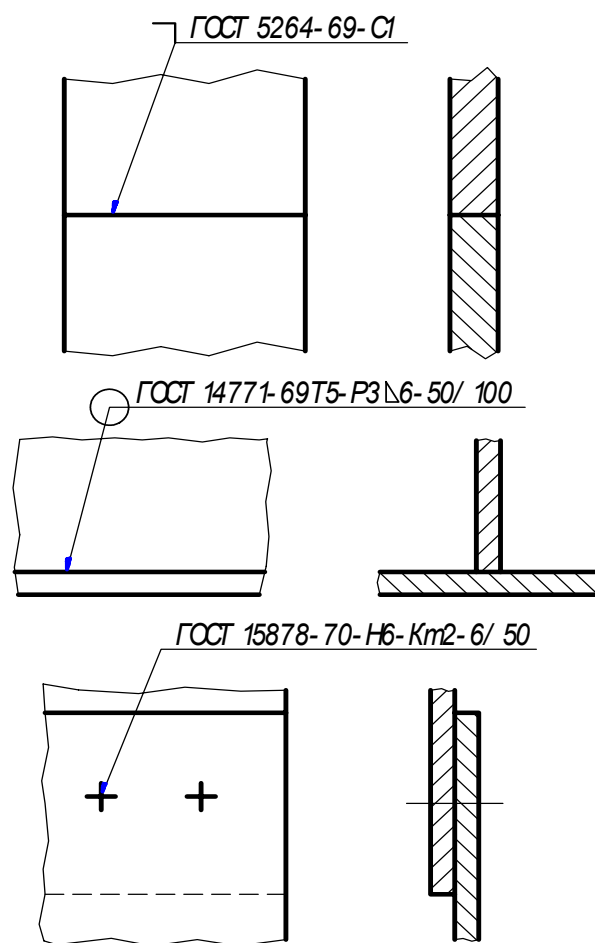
Условные обозначения стандартных швов сварных соединений
